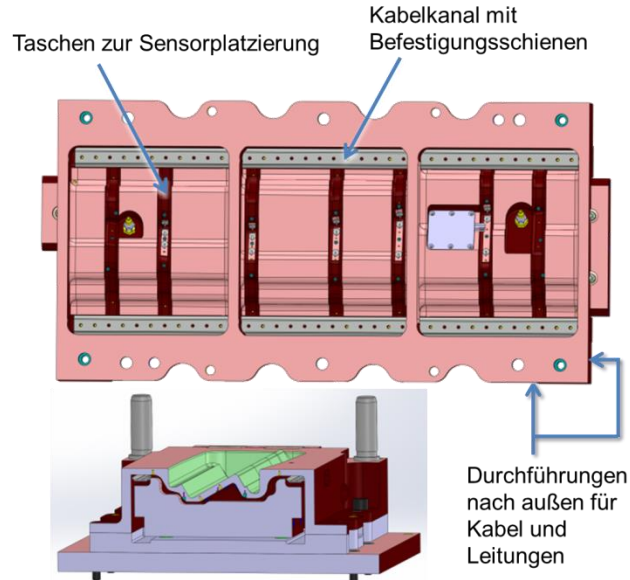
rückseitige Modifikation am Formwerkzeug zur Sensorintegration
